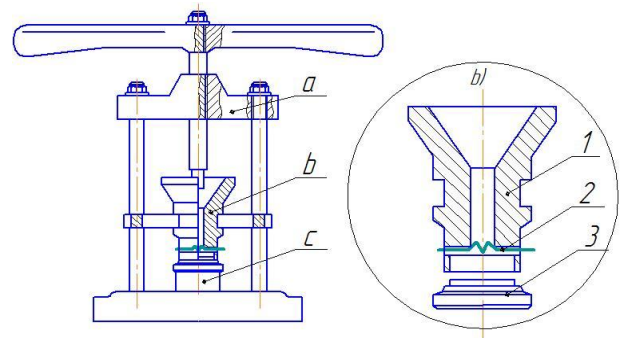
Конструктивна схема механічного преса для формування пробки:
